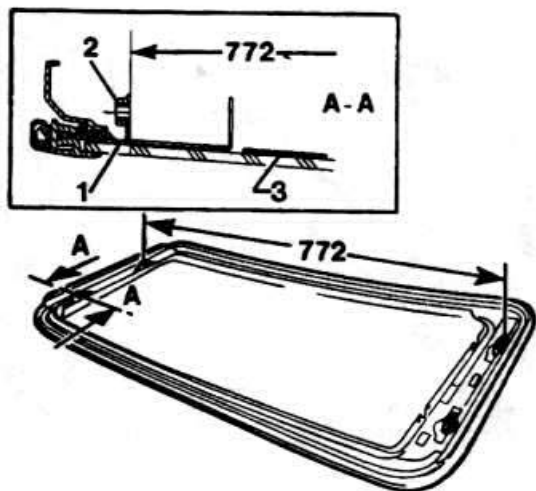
Размеры посадочного фланца панели сдвижной крыши:
